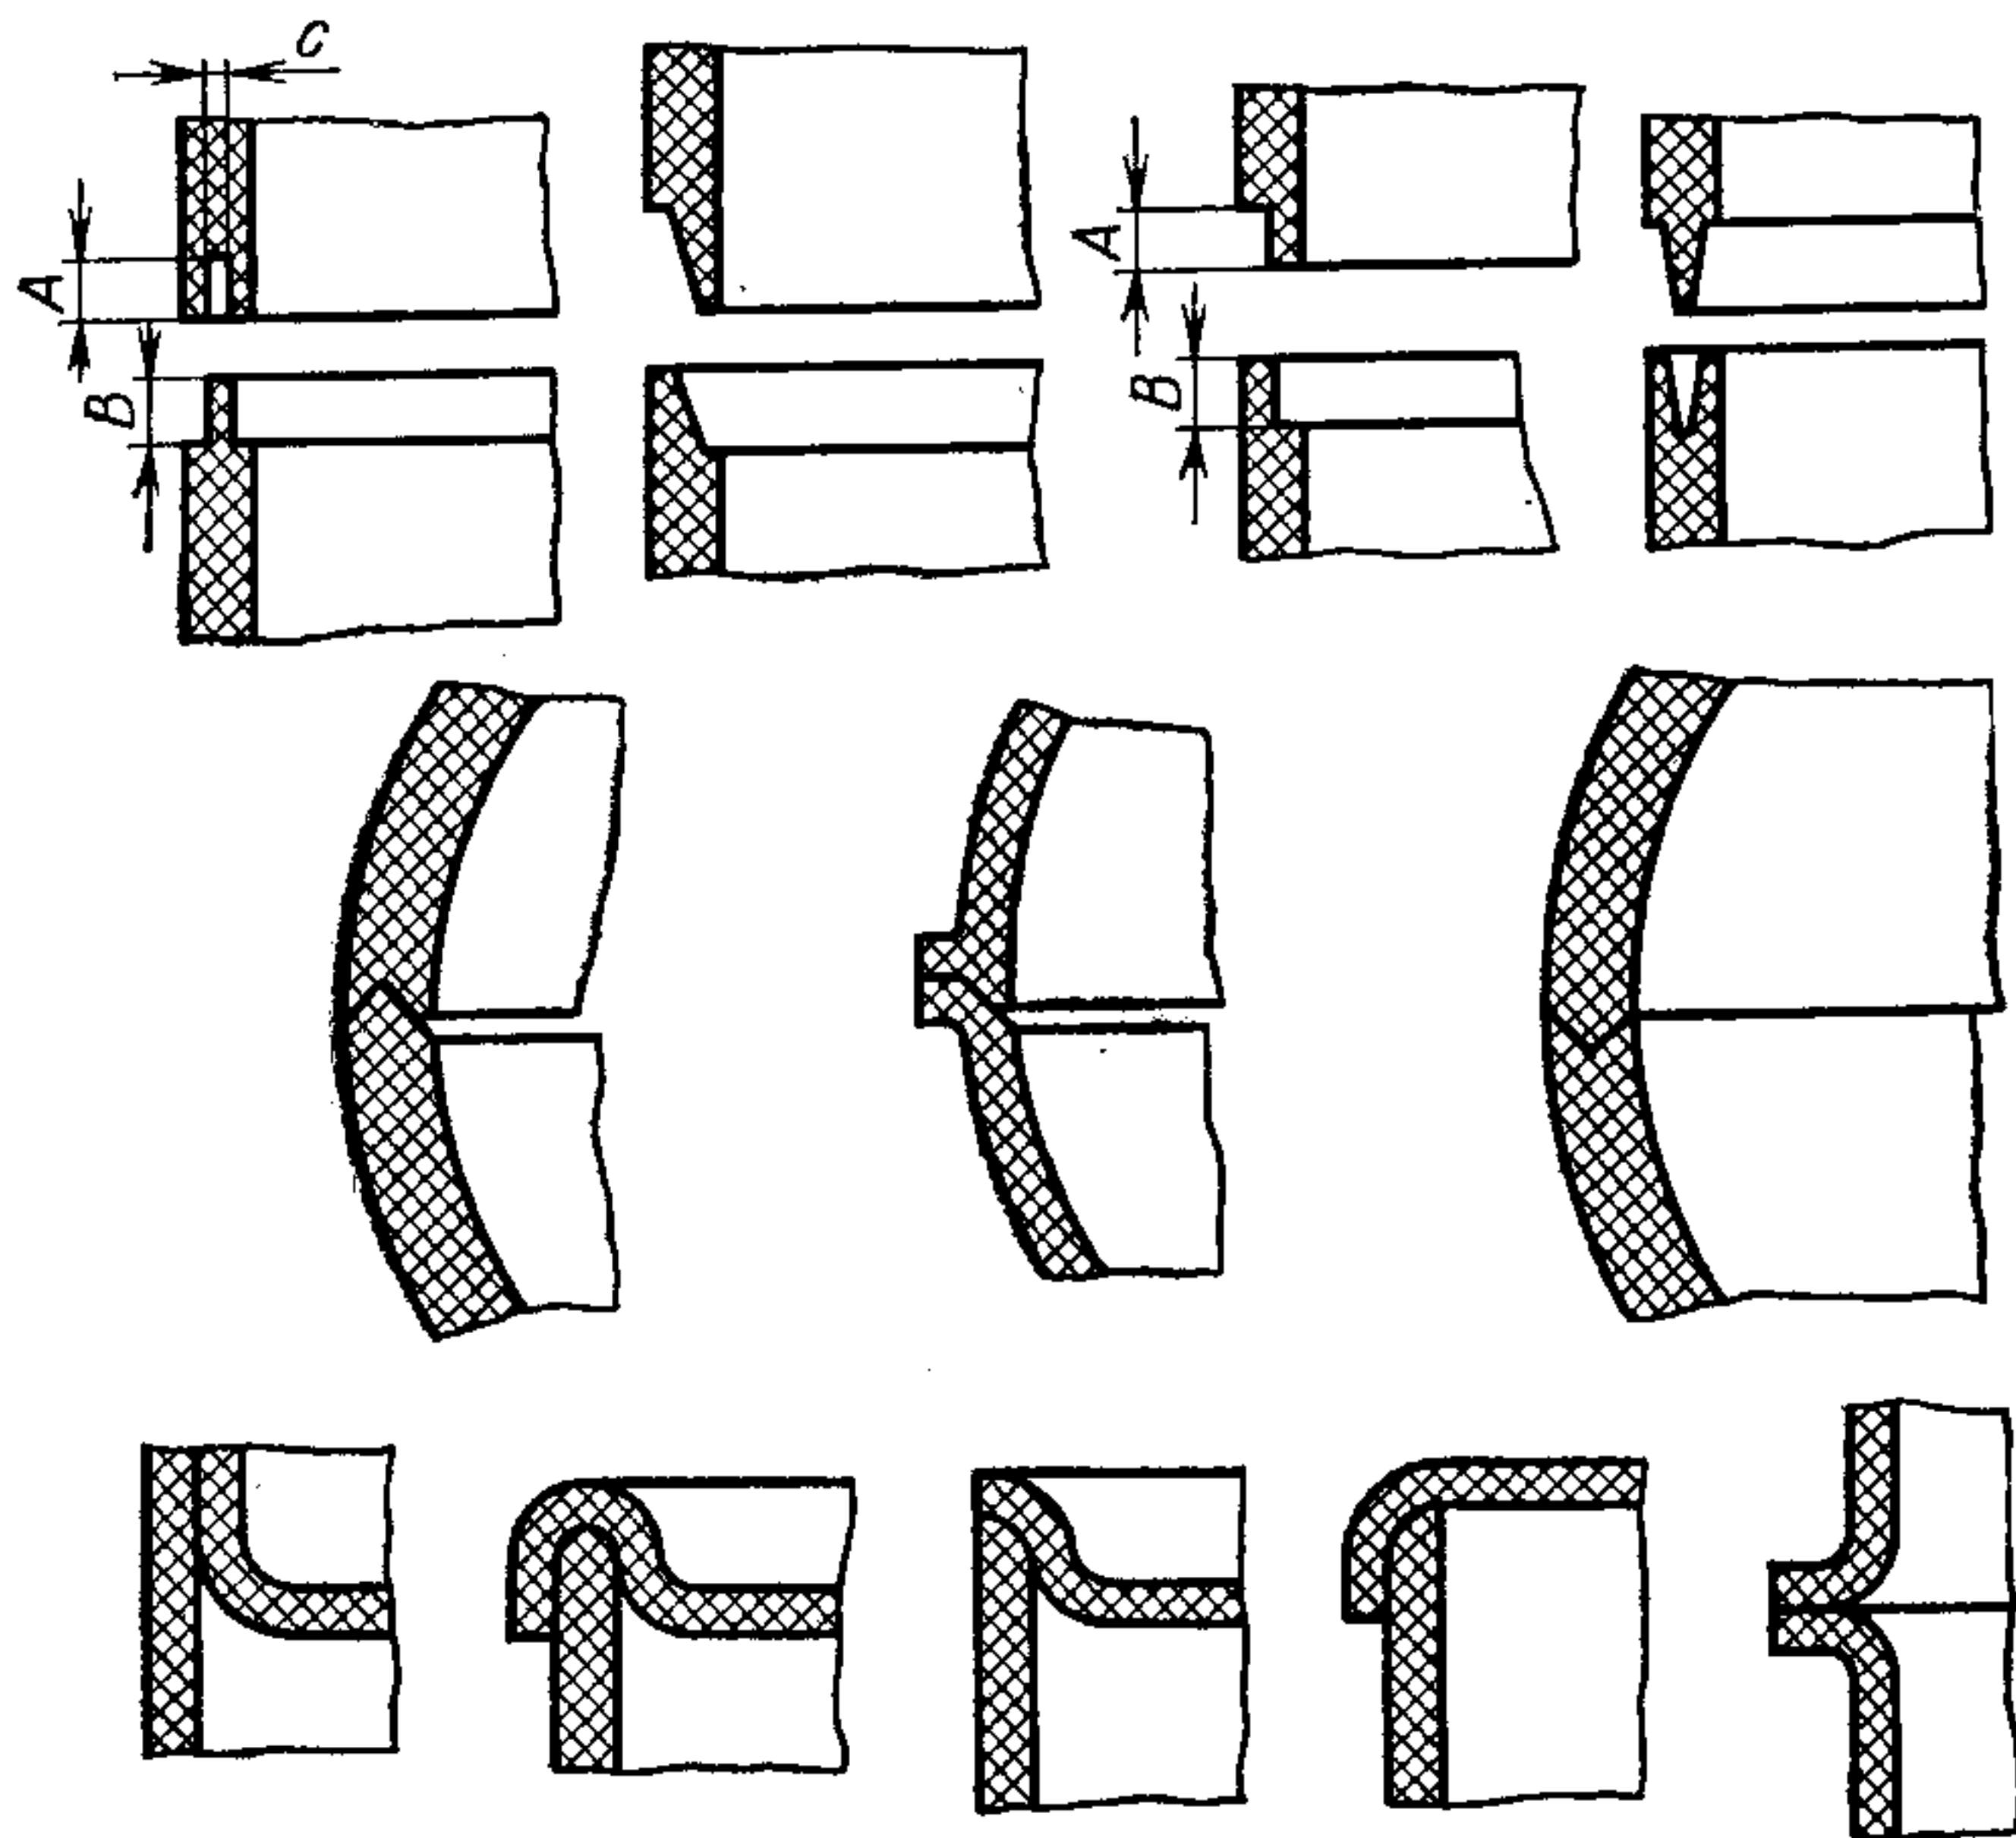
Варианты разделки кромок при соединении деталей (типа тел вращения) сваркой трением
